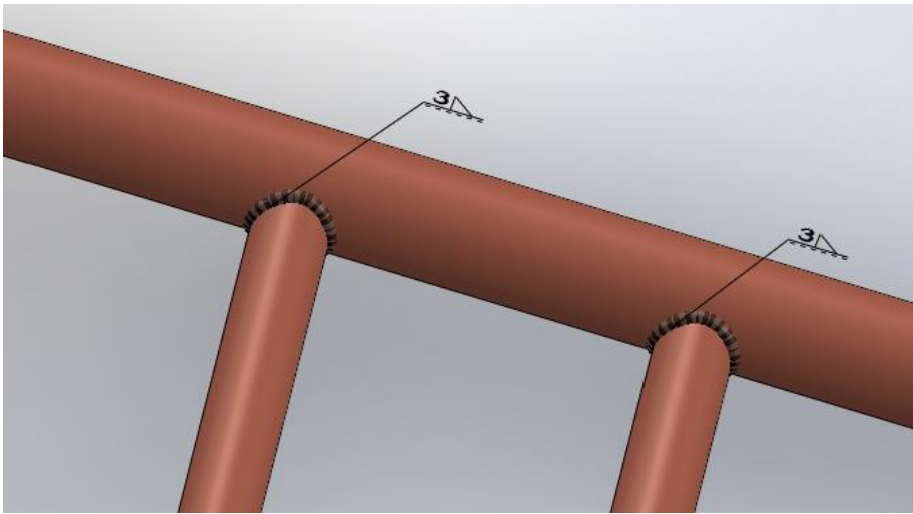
Unión por soldadura de los tubos verticales y horizontales
